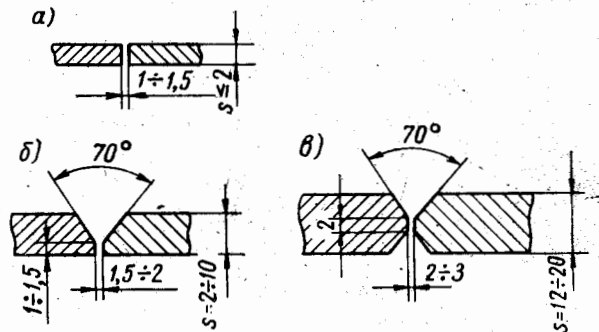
Конструктивные элементы подготовки кромок листовой латуни марки Л62, свариваемой встык газовой сваркой (по ОН 26-01-71—68): а — без скоса кромок; б — V-образная разделка кромок; в — X-образная разделка кромок
